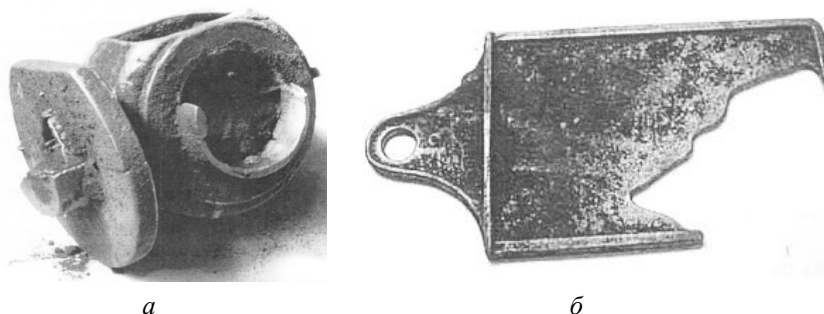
Виливки з дефектом «Недолив»: а – «Корпус вентиля»; б – «Засувка»
